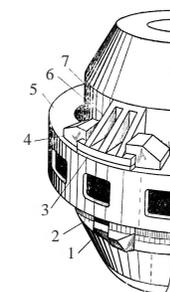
Крепление корпуса конвертера к опорному кольцу посредством кронштейнов: 1, 4 – фиксаторы боковых смещений, 2 – опоры, 3 – плита, 5 – опорное кольцо, 6 – кронштейн, 7 – корпус
